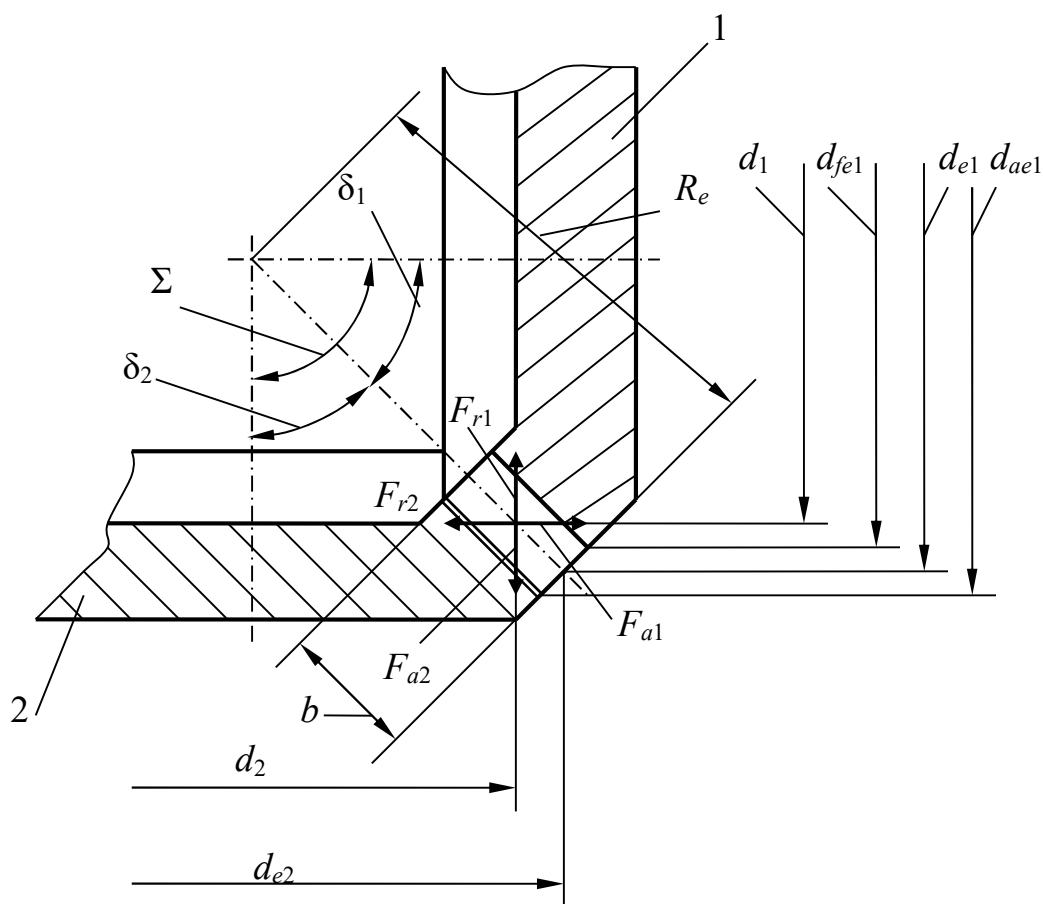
Основные геометрические параметры конической зубчатой передачи
